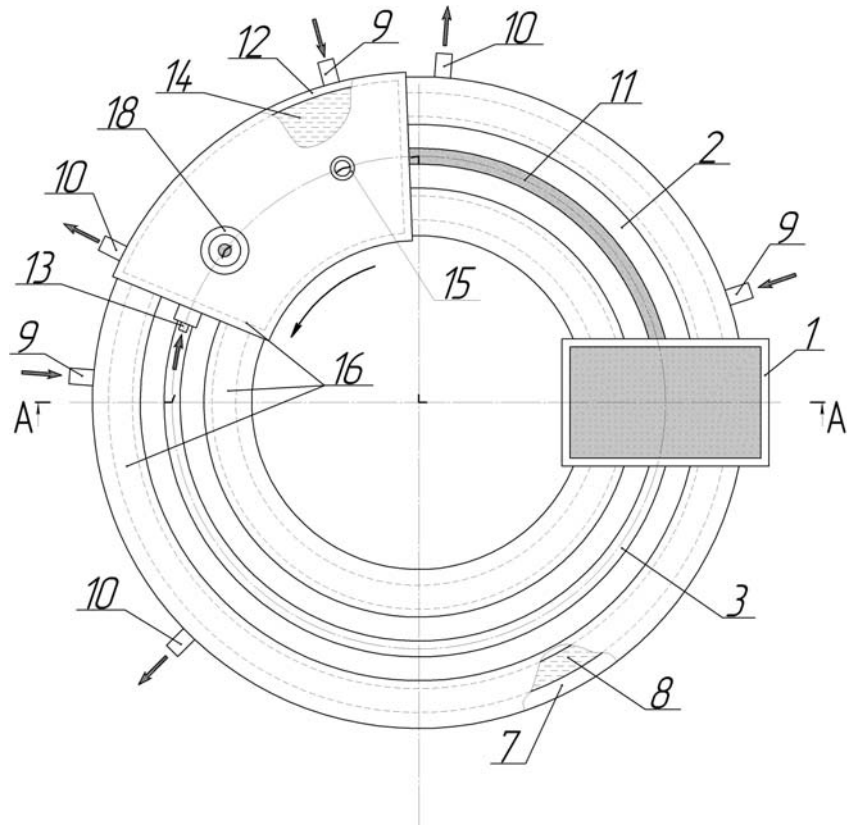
Вид сверху устройства для непрерывного литья и прессования лигатурного прутка для модифицирования алюминиевых сплавов методом конформ
